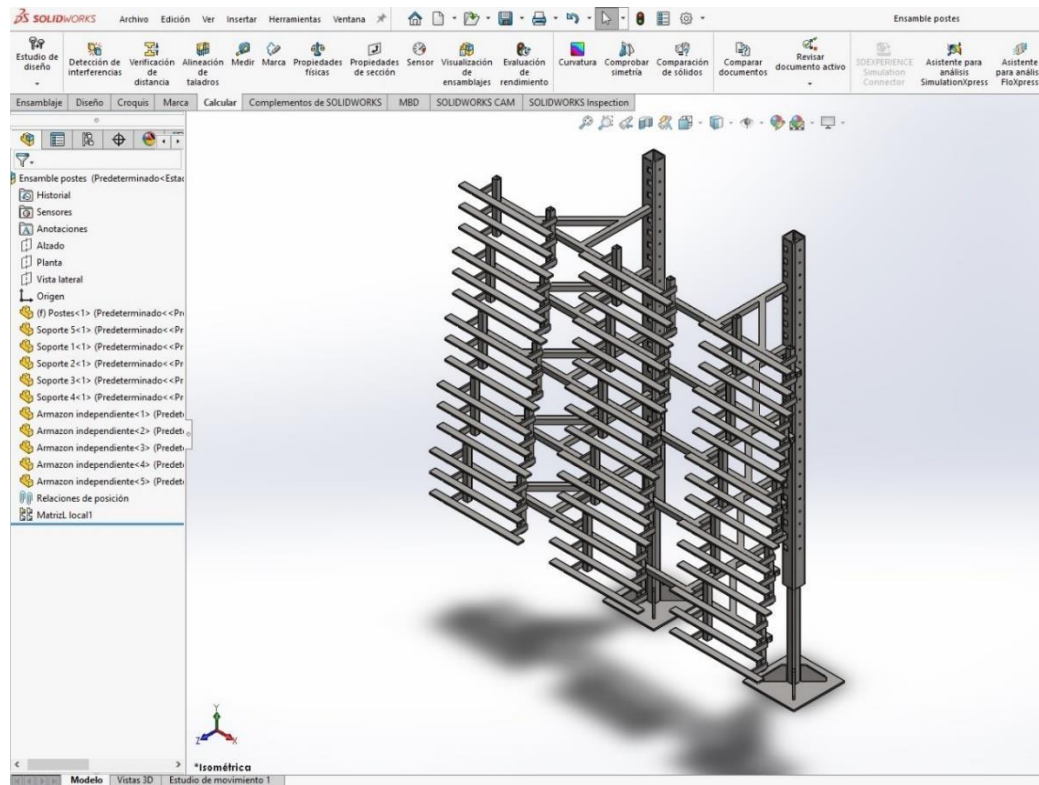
Ensamblado final para pintar, ensamblar u operar en autopartes plásticas. Esta muestra los soportes desarrollados, así como el Armazón o Fixture a utilizar. Todos los componentes van soldados.
